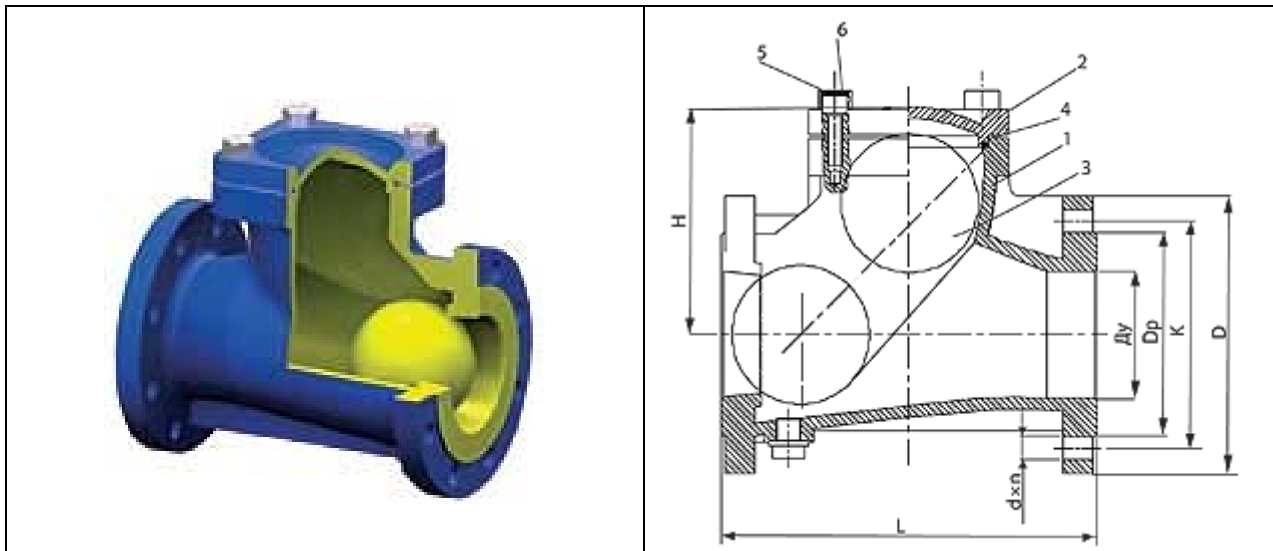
Обратный клапан шаровой V6516, Ду 50-500, Ру 10
